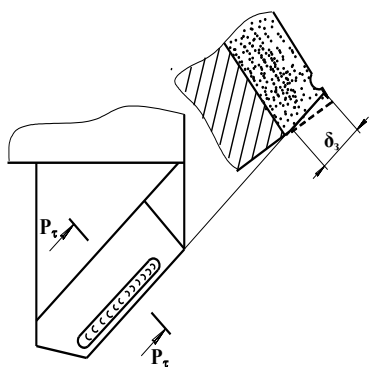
Схема зношування ножа торцевої твердосплавної фрези
